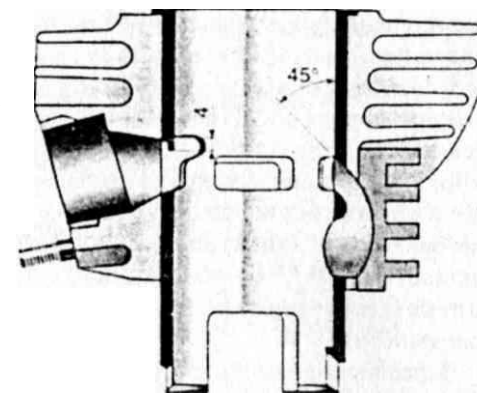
Доработанный цилиндр с новой гильзой, увеличенными окнами и двумя дополнительными продувочными каналами.
